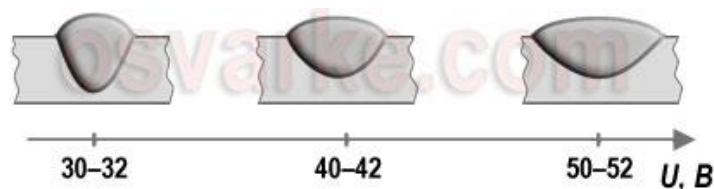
Влияние напряжения дуги на форму и размеры сварного шва
